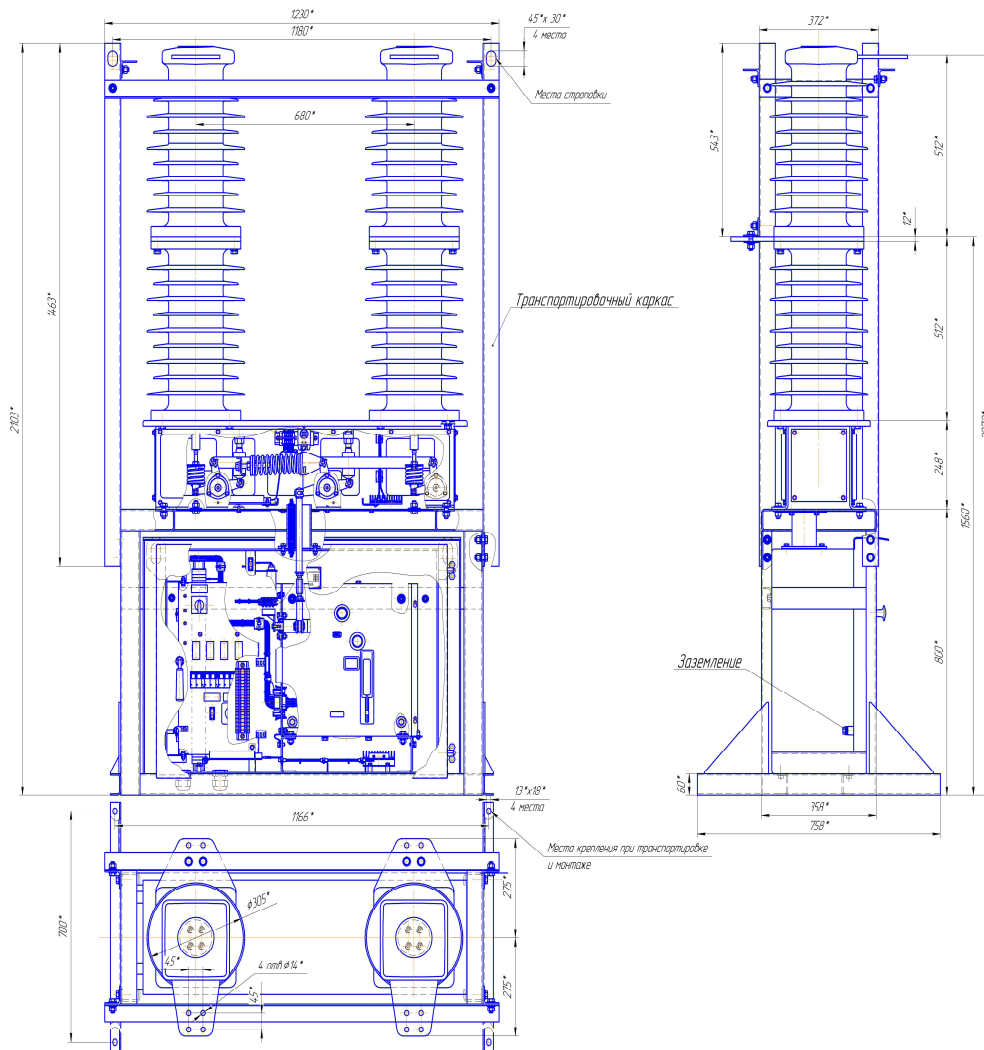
Габаритные, присоединительные и установочные размеры выключателя типа ВВН-СЭЦ-2-Э-35
